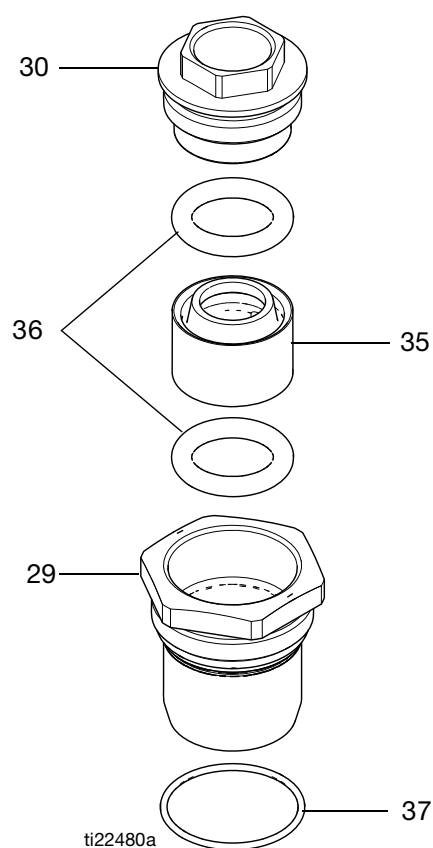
Démontage ou montage de la cartouche de presse-étoupe
